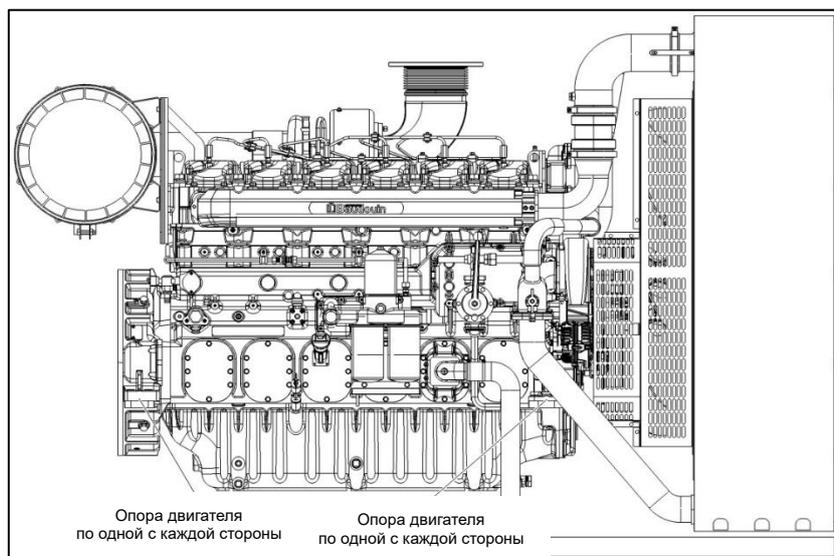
А-Опоры двигателя 6M26 (показанный насос прокачки - опционально)
